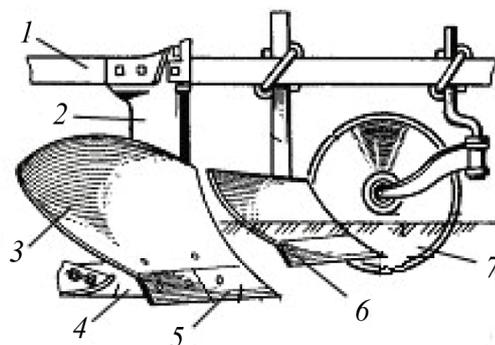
Рабочие органы плуга общего назначения: 1 – рама; 2 – стойка; 3 – отвал; 4 – полевая доска; 5 – лемех; 6 – предплужник; 7 – дисковый нож
